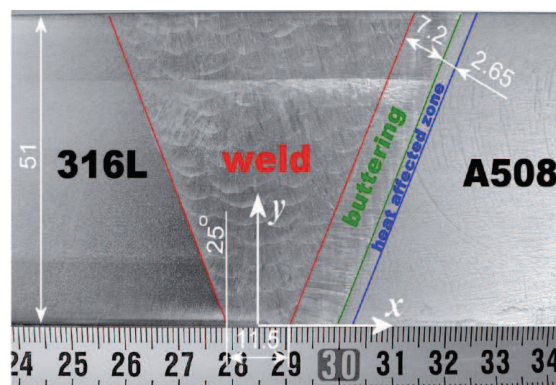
Soudure ADIMEW [GIL 09-2]
